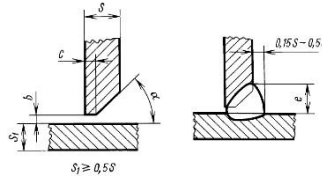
Зовнішній вигляд та підготовка крайок під зварювання таврового з'єднання Т6
